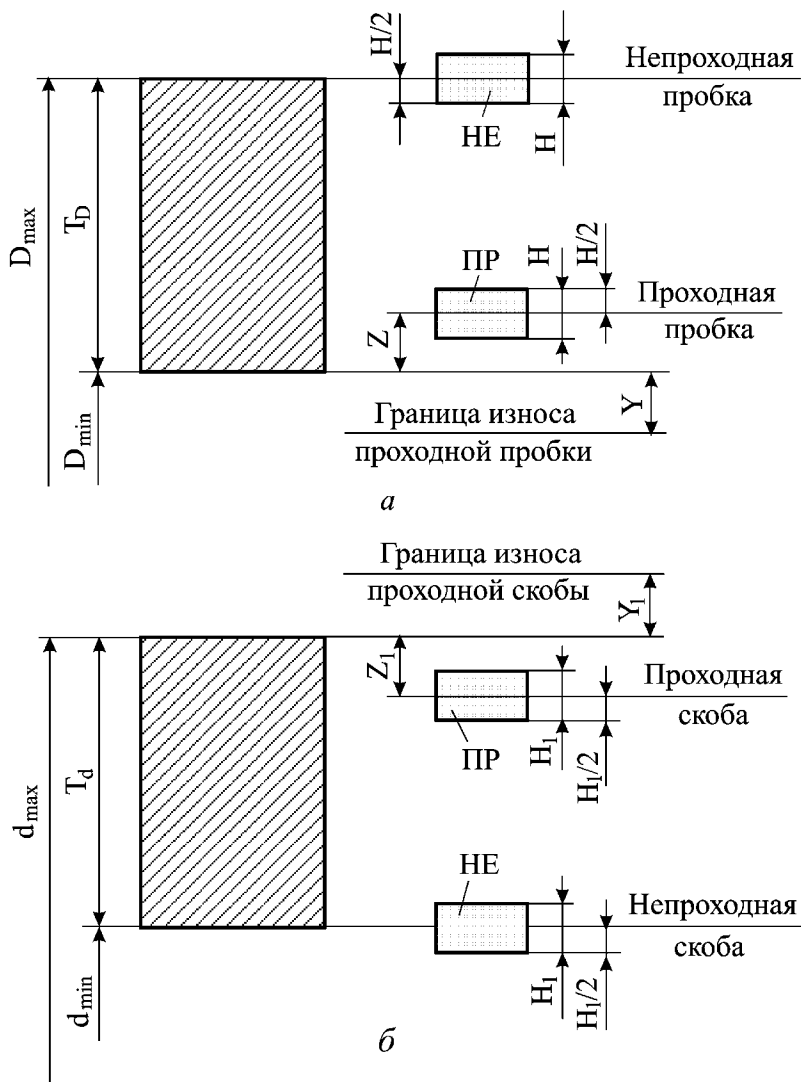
Схемы расположения полей допусков гладких калибров для контроля отверстий (а) и валов (б) с номинальными размерами до 180 мм и допуском изготовления по IT6-IT8
